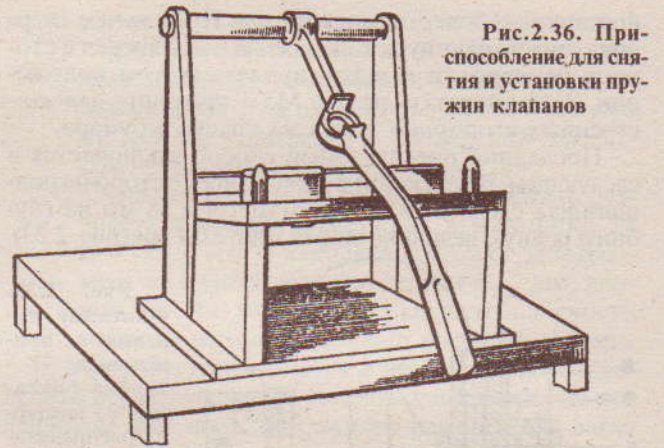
Приспособление для снятия и установки пружин клапанов
